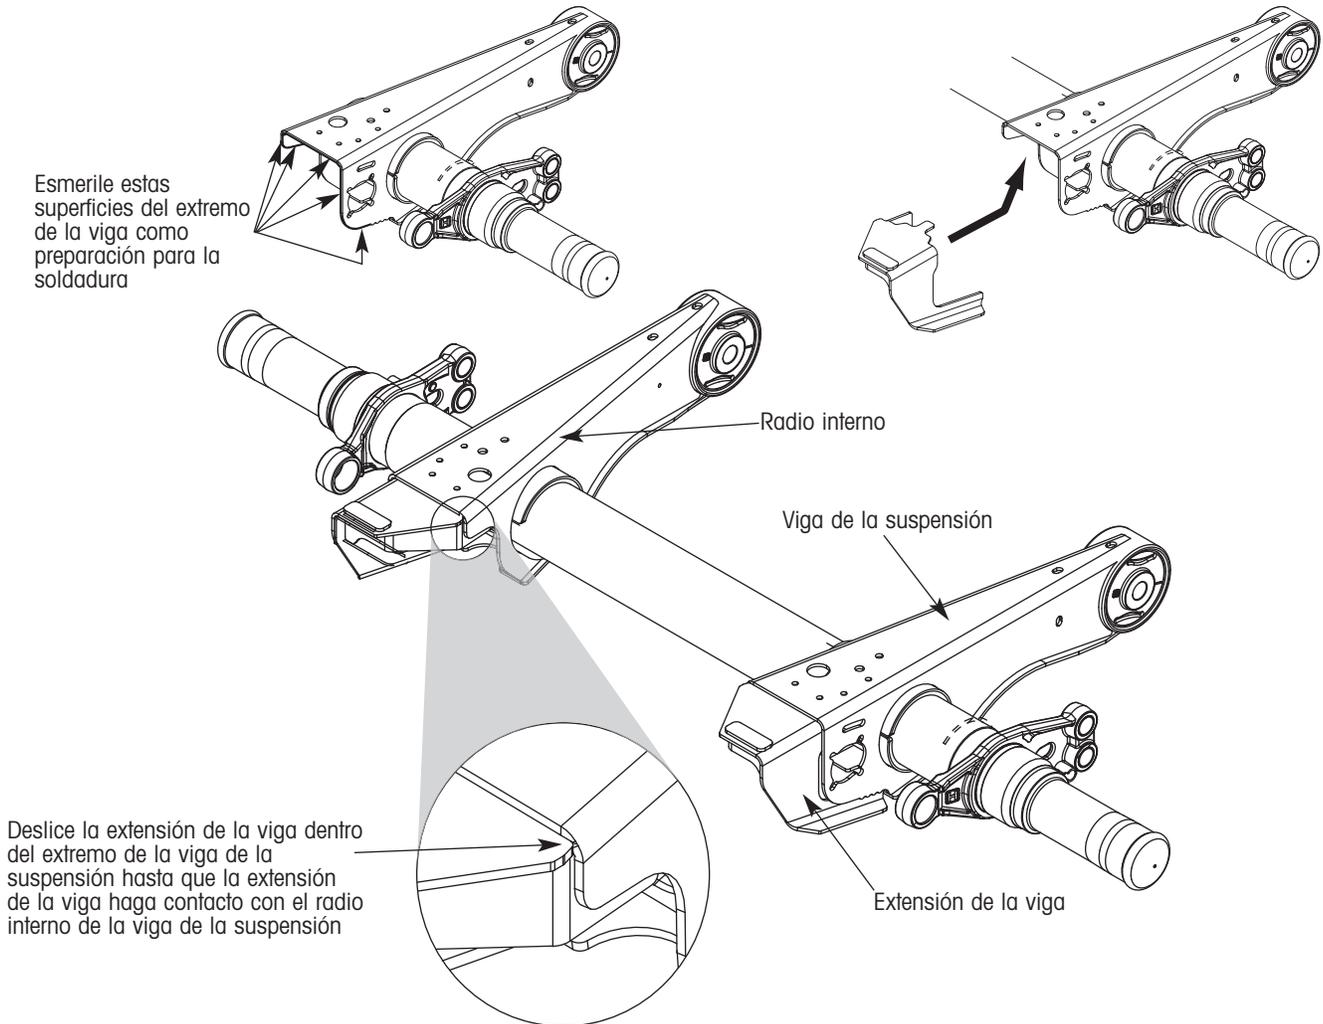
Preparación de las vigas de la suspensión HKANT 40K (HKA180) y HKANT 46K para la soldadura e instalación de las extensiones de la viga
